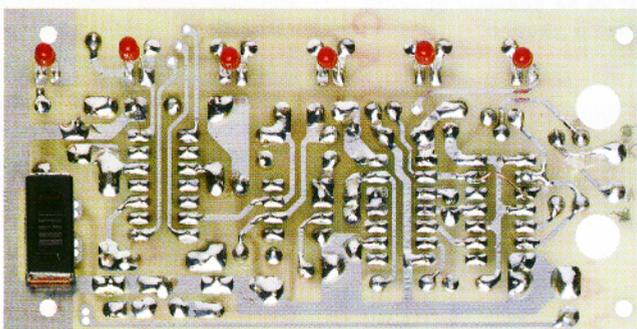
Photo d'un des prototypes de la platine du Diode Speed Tester, vu côté soudures.
